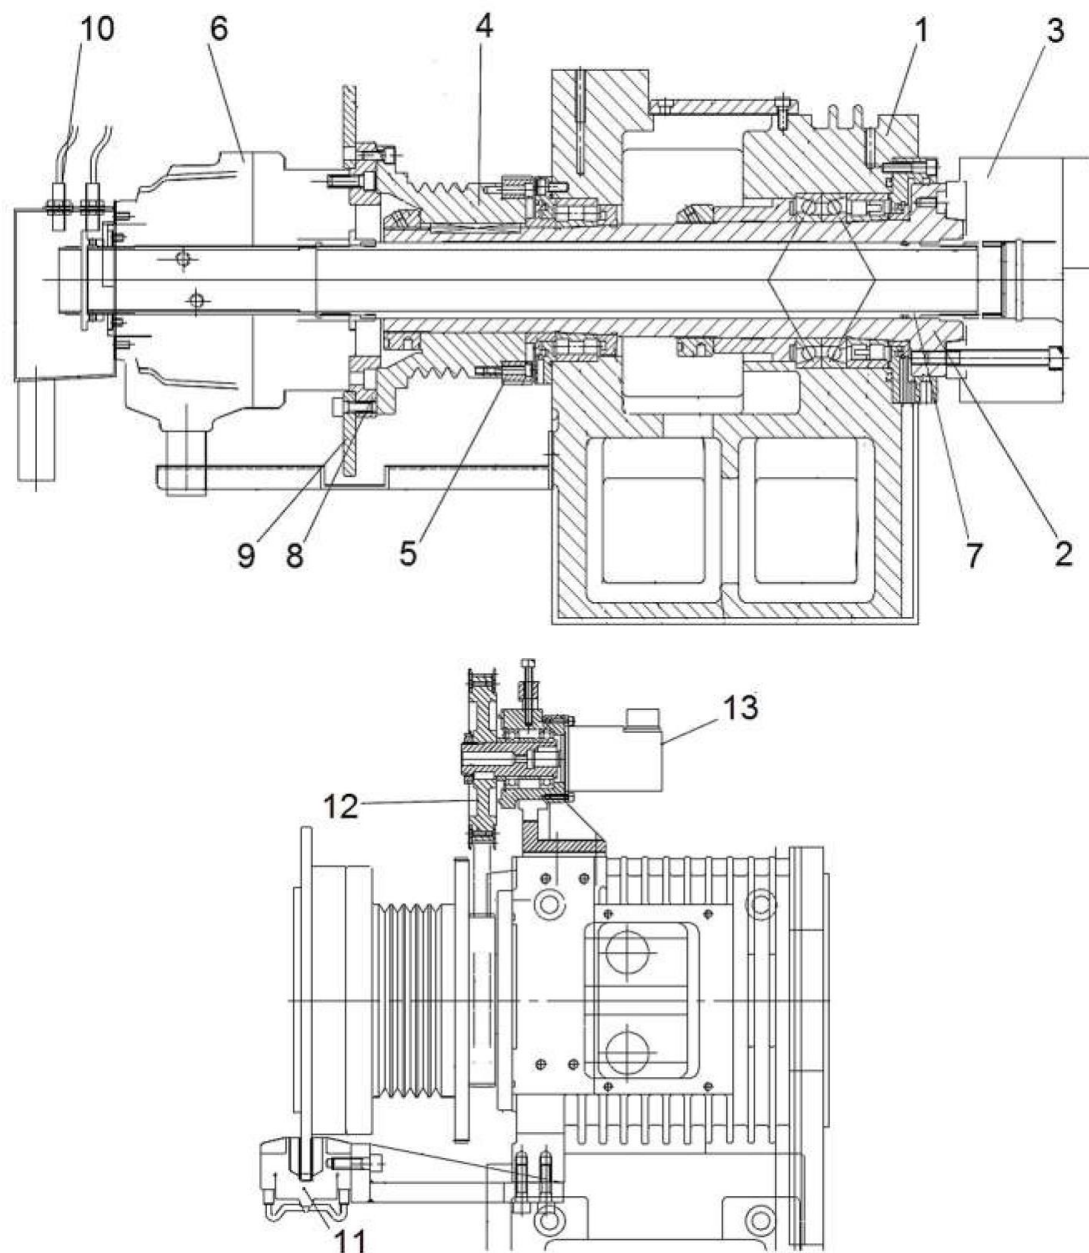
Конструкція шпиндельного вузла із гальмівним пристроєм та датчиком положення шпинделя
